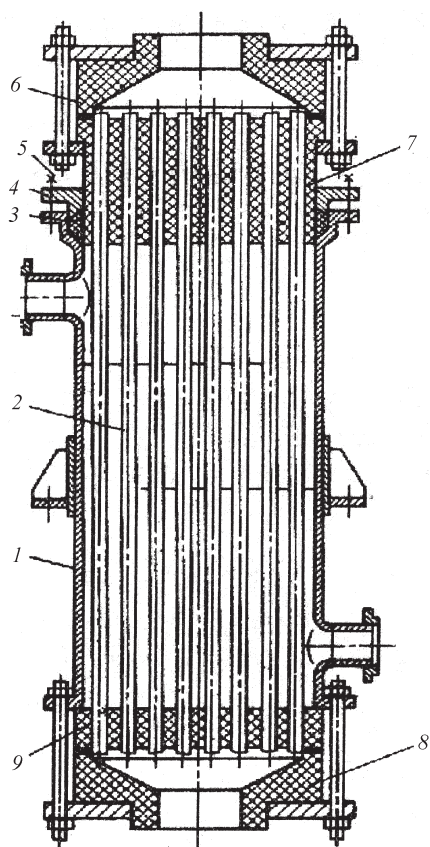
Кожухотрубный углеграфитовый теплообменник: 1 — металлический кожух; 2 — трубный пучок; 3 — сальниковое уплотнение; 4 — нажимная втулка; 5 — шпильки; 6 — верхняя крышка; 7 — подвижная трубная решетка; 8 — нижняя крышка
